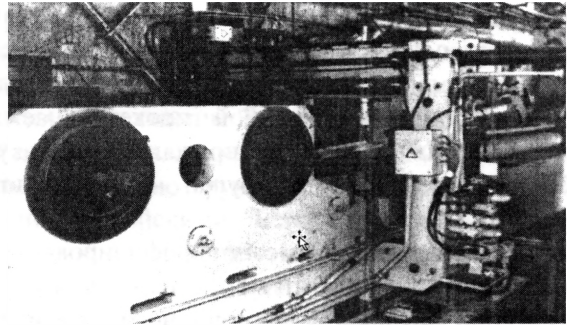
Стан для прокатки заготовок направляющих опор пневмоподвески
